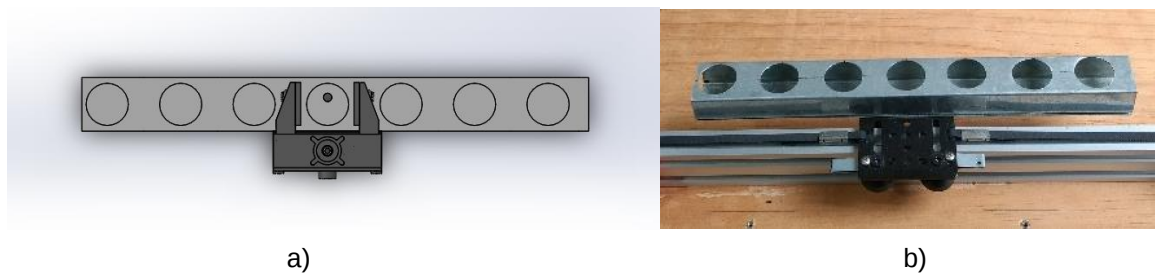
Rack de llenado a) Diseño en Solidworks® b) Rack construido
